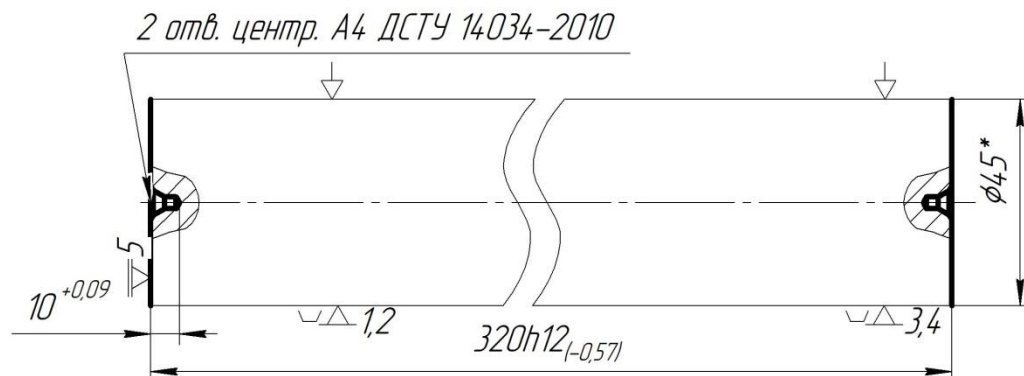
Схема установки заготовки в самоцентрувальні призми
